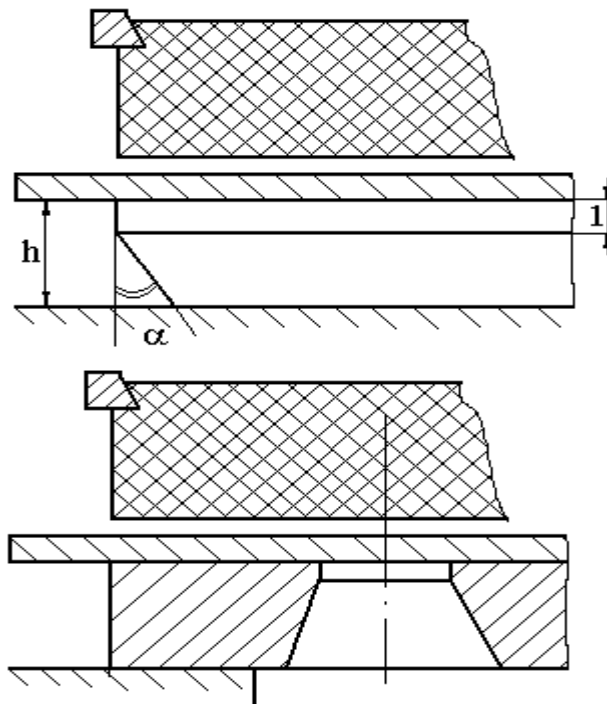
Схема штампов для вырубki-пробивки резиной:
